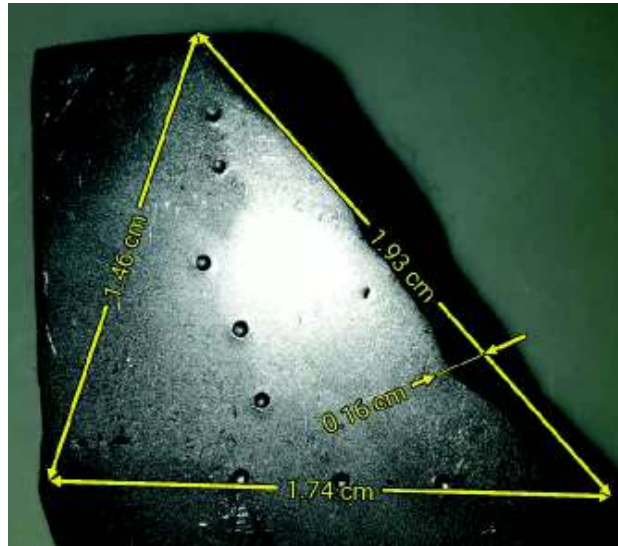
Dimensiones principales del cordón de soldadura (Longitud de pierna, convexidad y altura del cordón).
